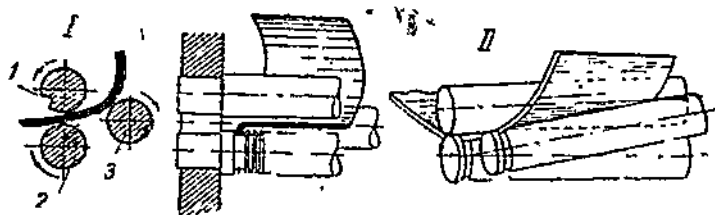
а. Схема прокатки листов для изготовления цилиндрических I и конусных II воздуховодов на трехвалковой ручной вальцовке.
